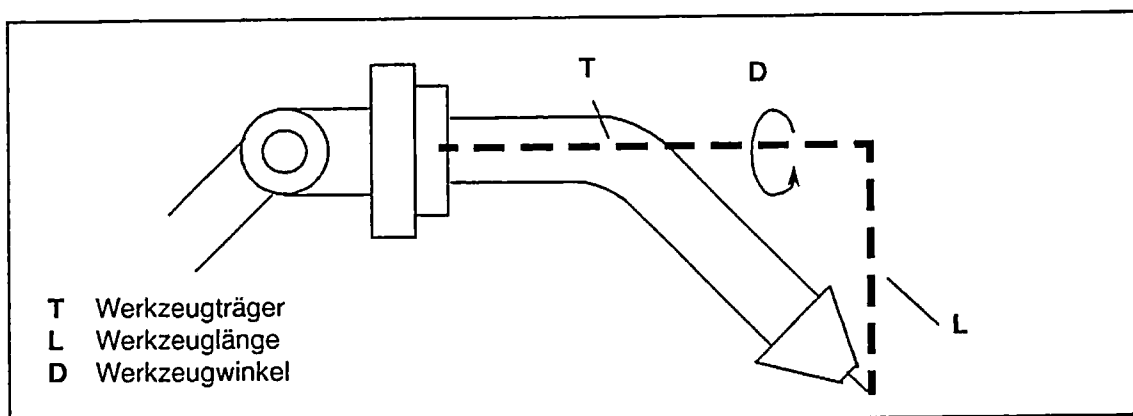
Werkzeugkorrekturdaten WZK 3D
